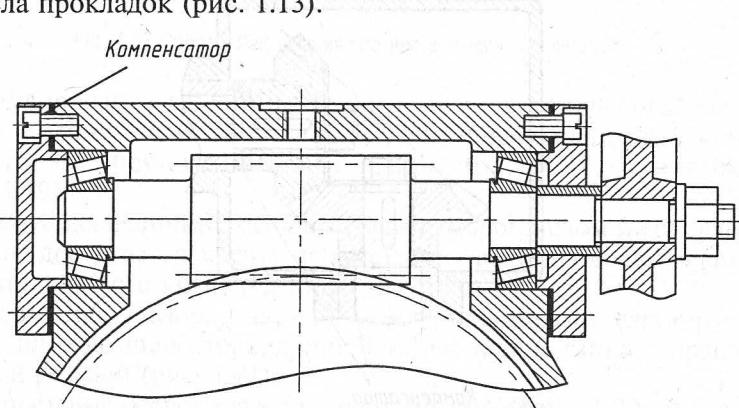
Способ регулировки осевого зазора в коническом роликовом подшипнике
